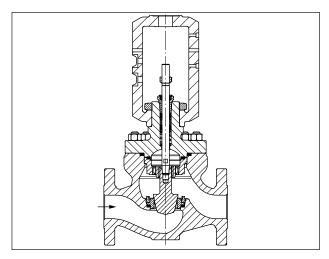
Durchgangsventil Typ 251GR mit geschraubtem Sitz
